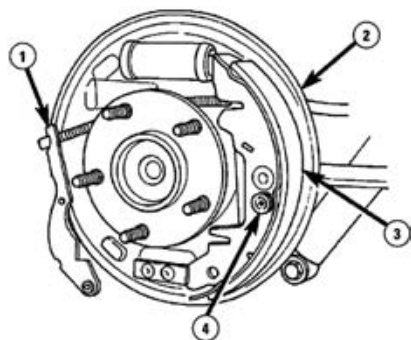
Барабанные тормозные колодки: 1 – ручной тормоз; 2 – пластина крепления колодок; 3 – ведущая колодка; 4 – крепление.
